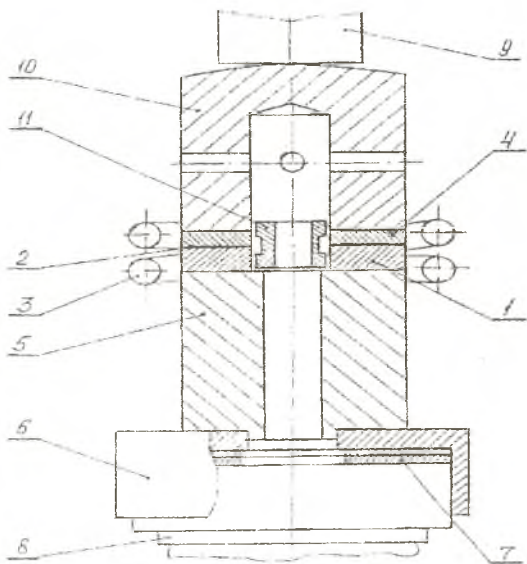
Оснастка для диффузионной сварки деталей биметаллического элемента модуля уплотнения: 1 – свариваемая деталь из титана, 2 – пакет прокладок (прослоек), 3 – индуктор, 4 – свариваемая деталь из стали, 5 – опорная втулка, 6 – центрирующий стакан, 7 – регулировочные прокладки, 8 – шток силового привода, 9 – упор вакуумной камеры, 10 – сферический колпак, 11 – технологическая центрирующая втулка
